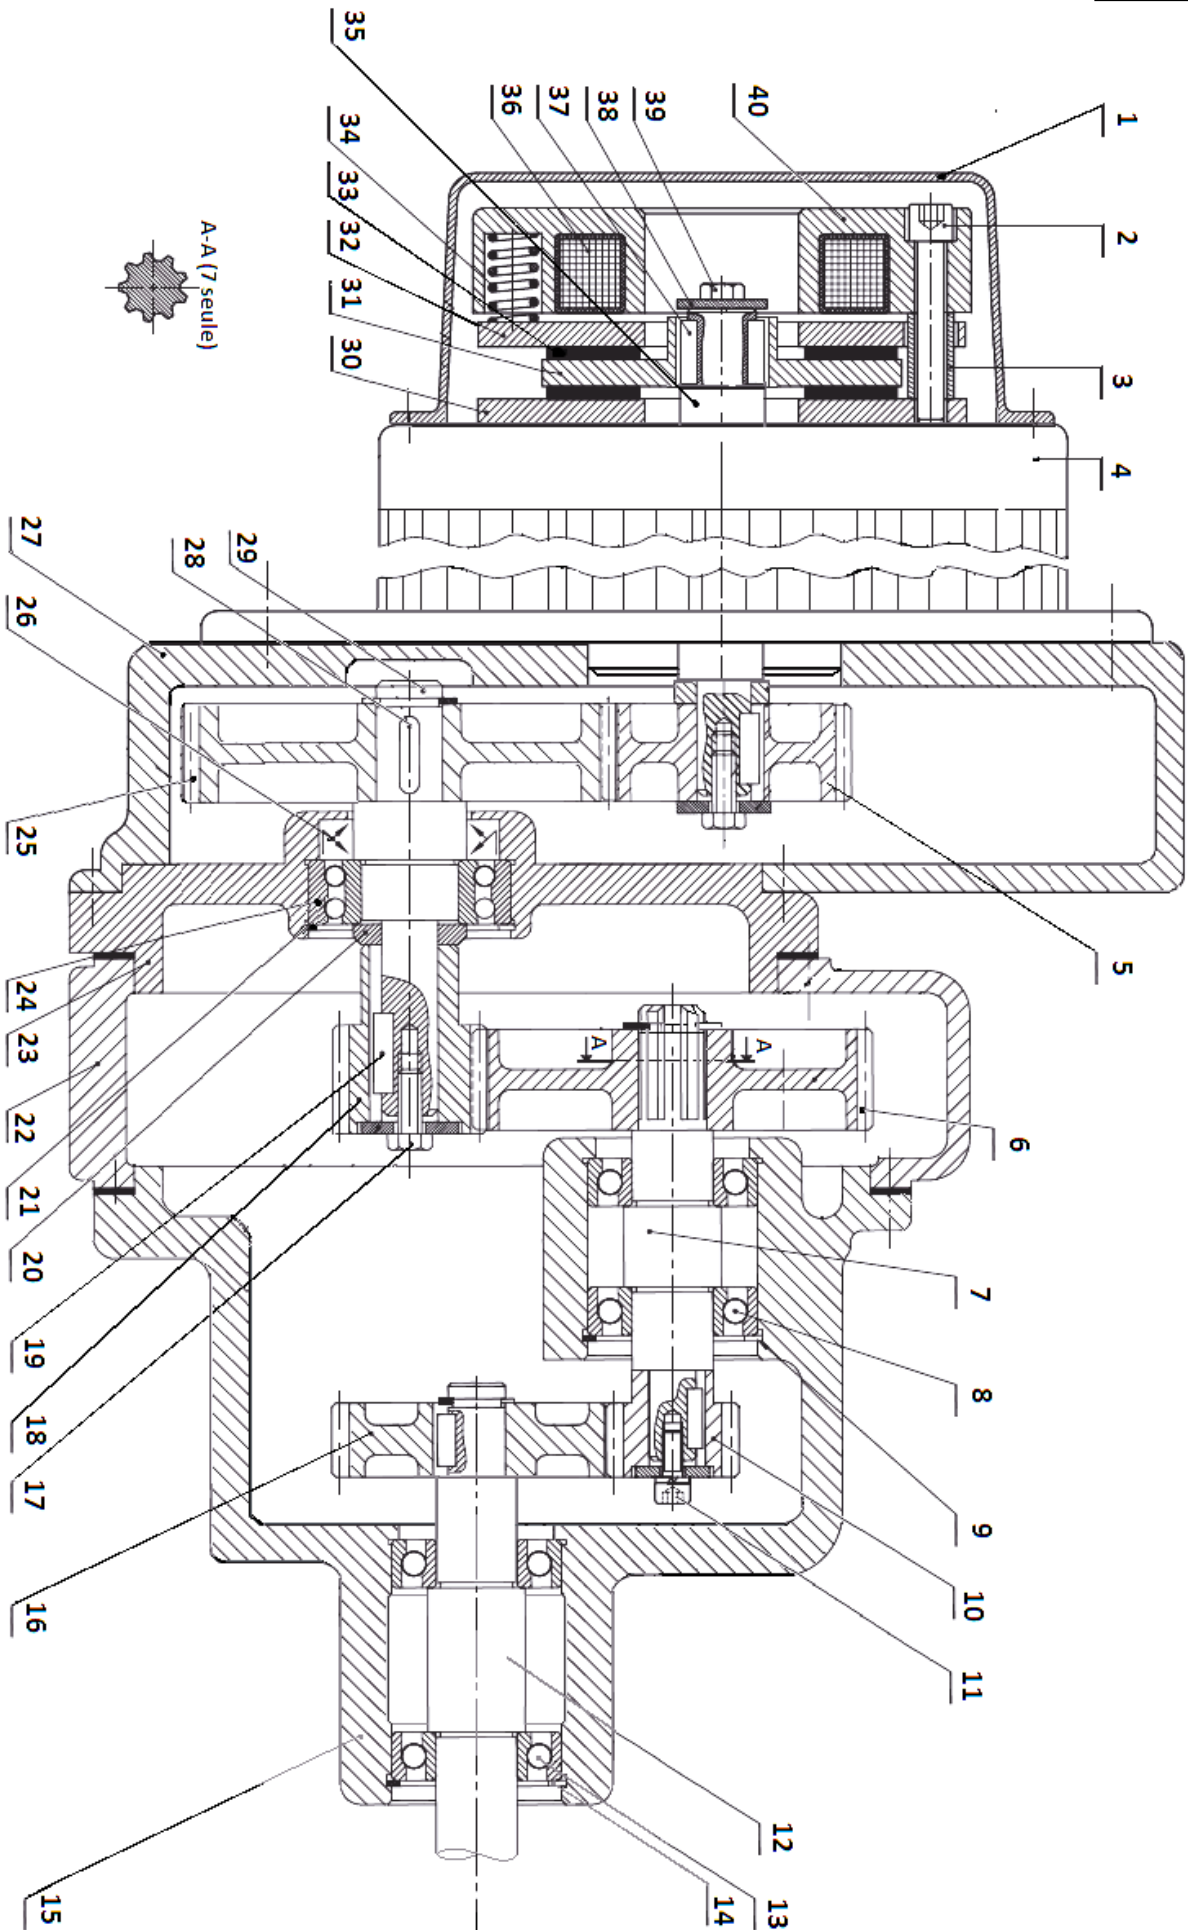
Dessin d'ensemble du moto-réducteur-frein
